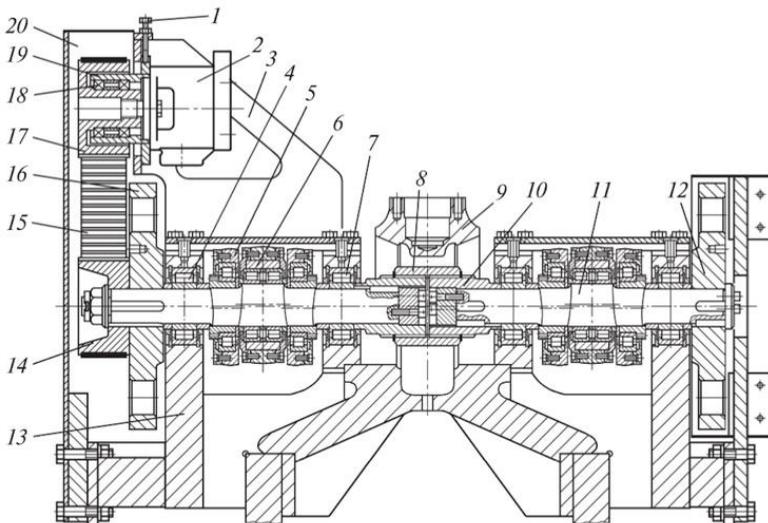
Узел установки эксцентрикового вала подбивочного блока машины ВПР-09-32 [3]:
